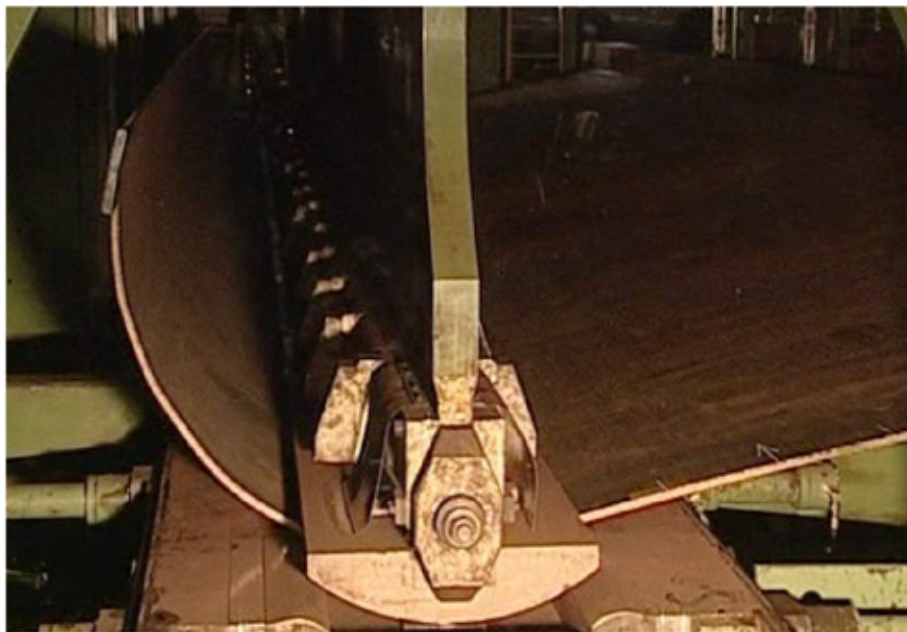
Изгиб плоской заготовки трубоформовочным прессом
